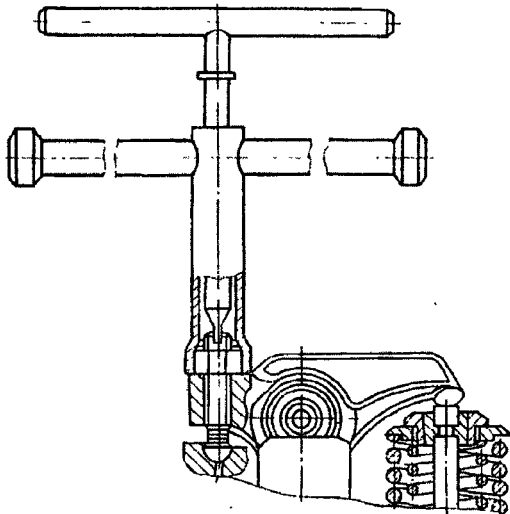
Приспособление И801.14.000 для регулирования клапанов двигателя
